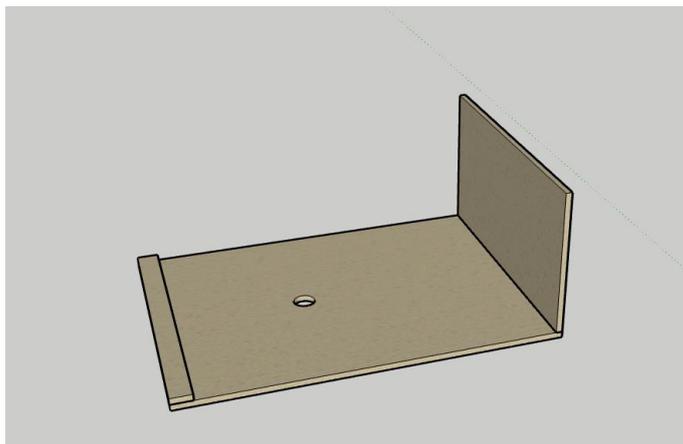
Base que manterá a caixa de engrenagens inclinada.
